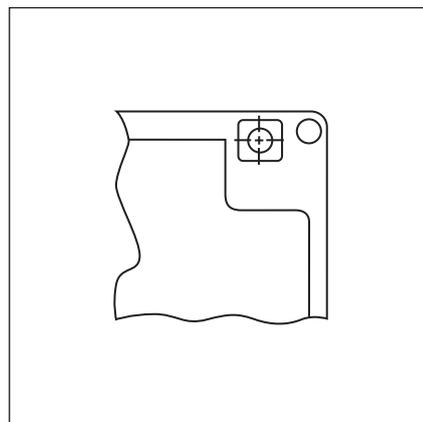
Befestigungslöcher des Gehäuses nutzen
